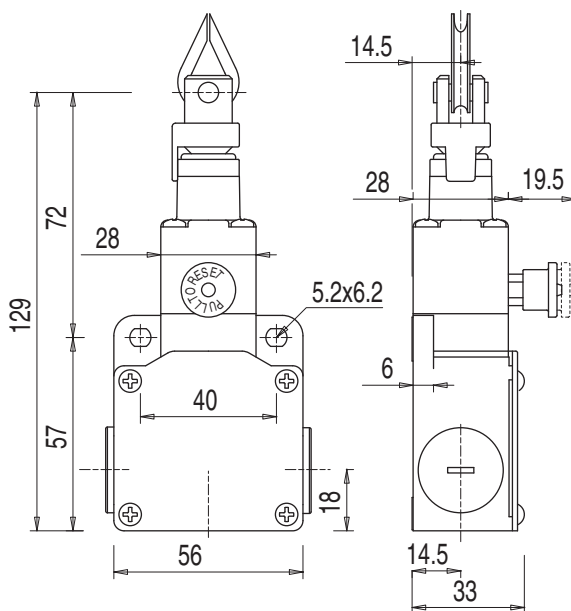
Dimensões do ERS-MxC3x-HLR em mm
